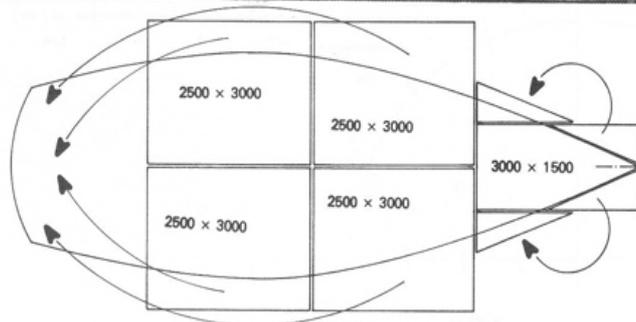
Devant de roof. Les tôles de pont et de toit de roof sont posées puis découpées. Ensuite, on mettra en place les tôles de l'hiloire.
